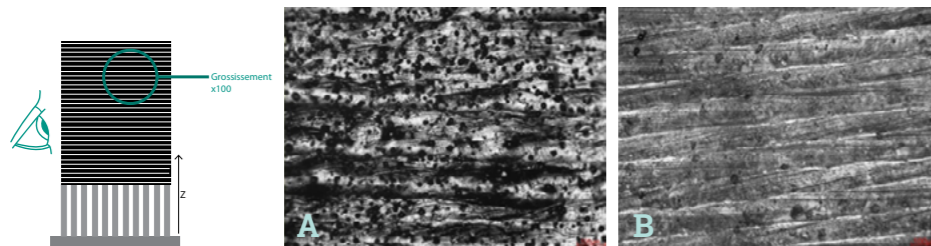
Textures de surfaces de composants fabriqués en Inconel par Fusion de poudre métallique par laser
